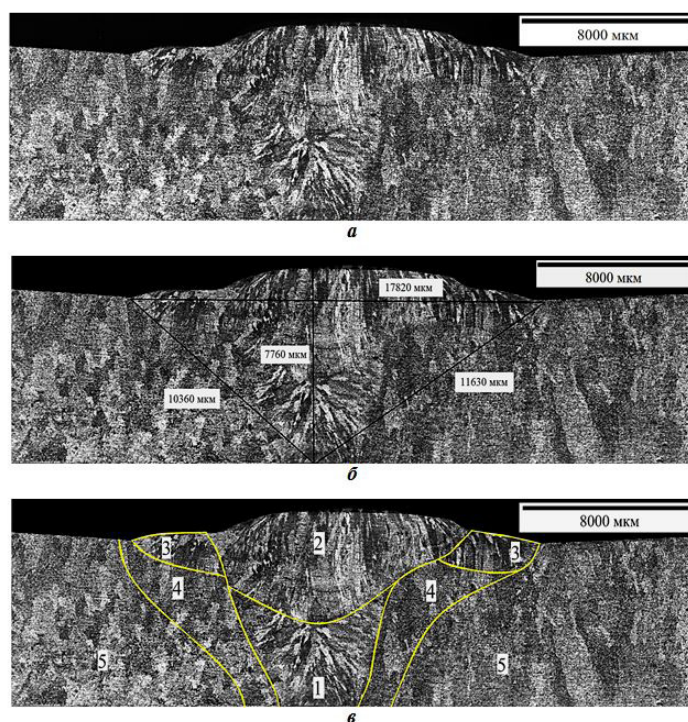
Макроструктура сплава в поперечном сечении трубного сварного соединения: *a* – общий вид; *b* – вид с размерами металла шва; *c* – вид с выделенными границами различных участков сварного соединения: 1 – первый (корневой) валик, 2 – второй валик, 3 – участок усиления шва, 4 – зона термического влияния, 5 – основной металл
